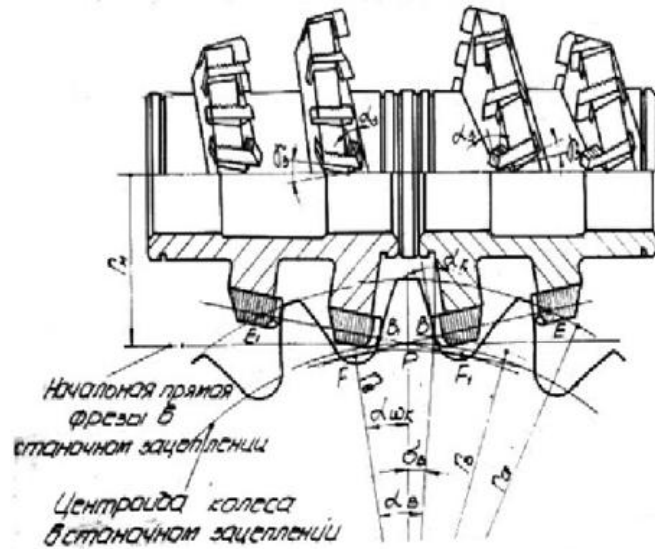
Технологическая схема резания фрезы с раздельной схемой формообразования шевронных зубчатых колес
